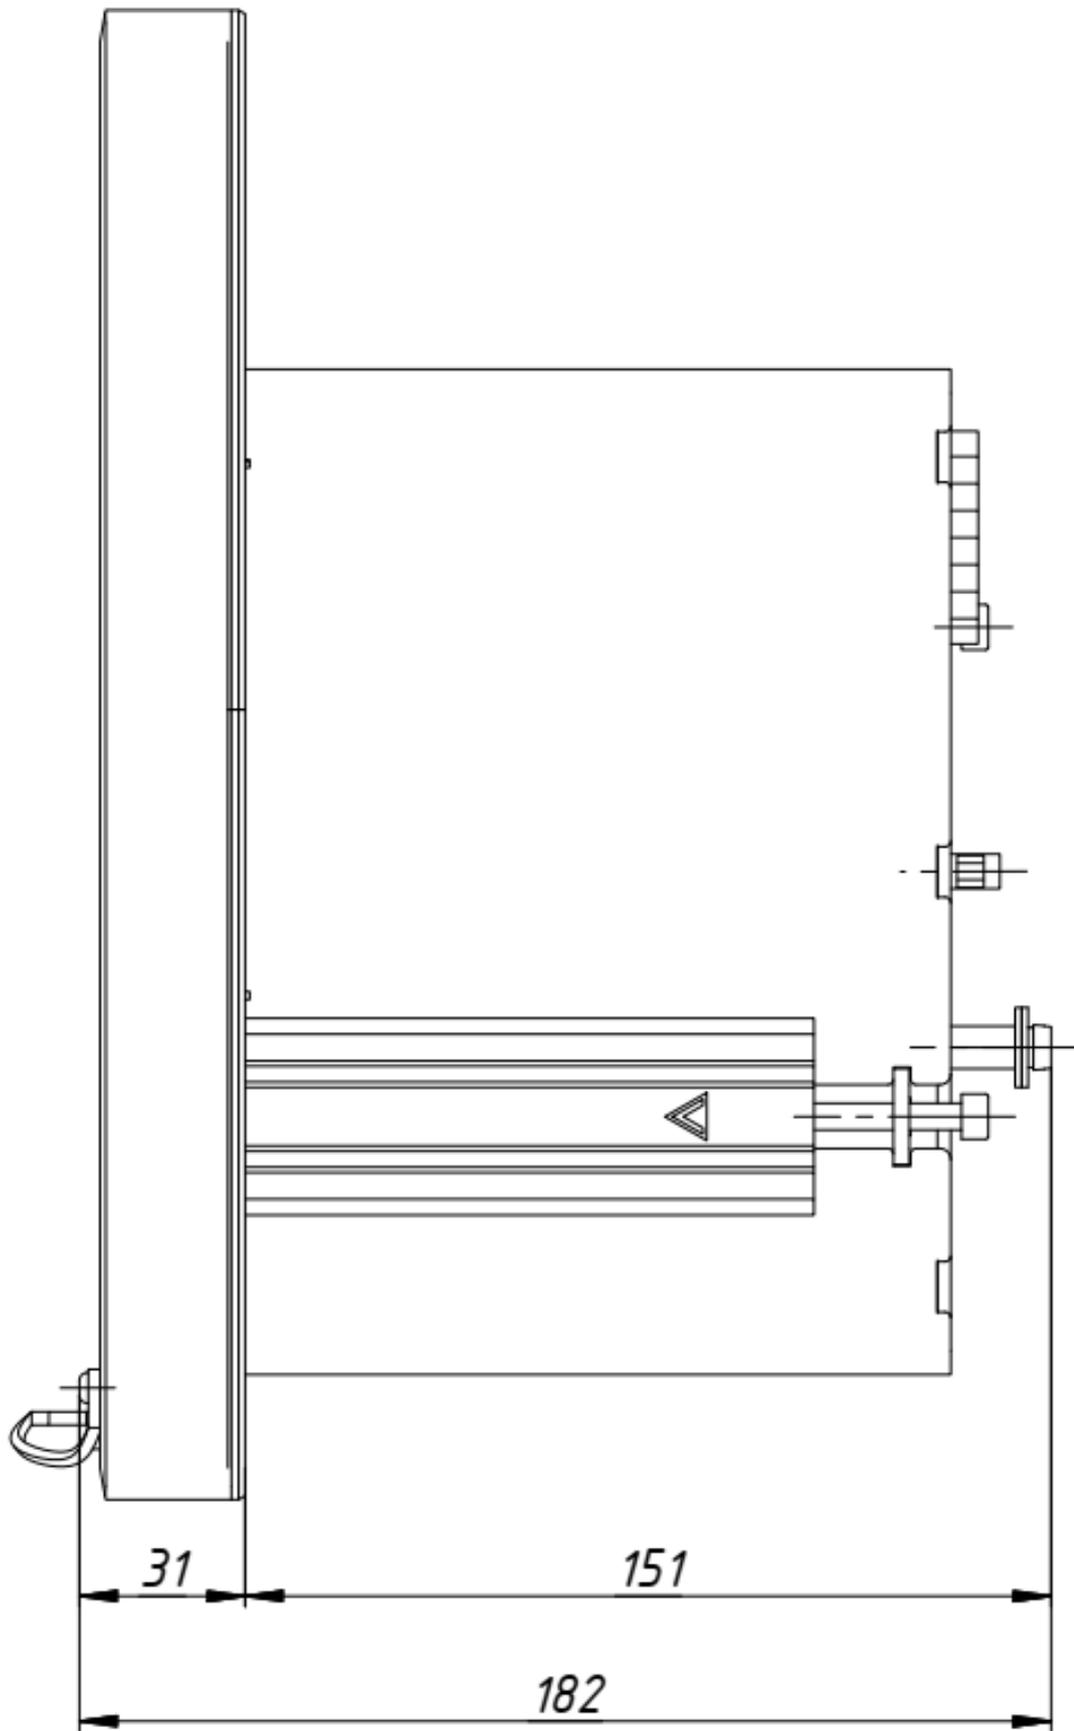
Габаритный чертёж прибора в исполнении Ф1772–4, вид сбоку
